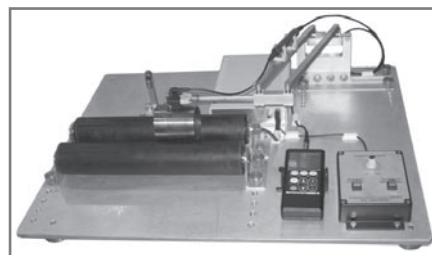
Механизированная установка для контроля резьбы УКР-ВТ1
